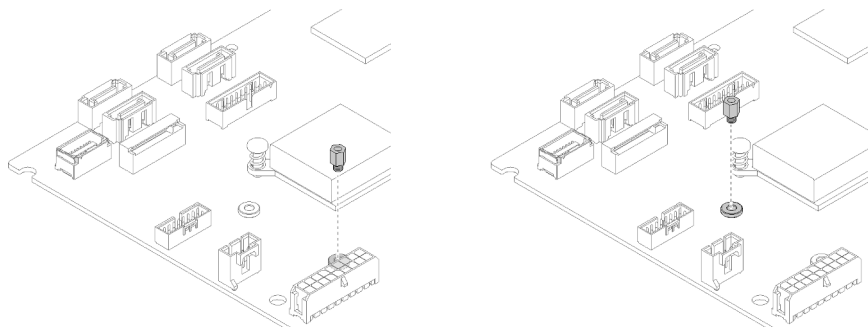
Emplacement de la vis hexagonale pour l'unité M.2 de 80 mm ou 42 mm
